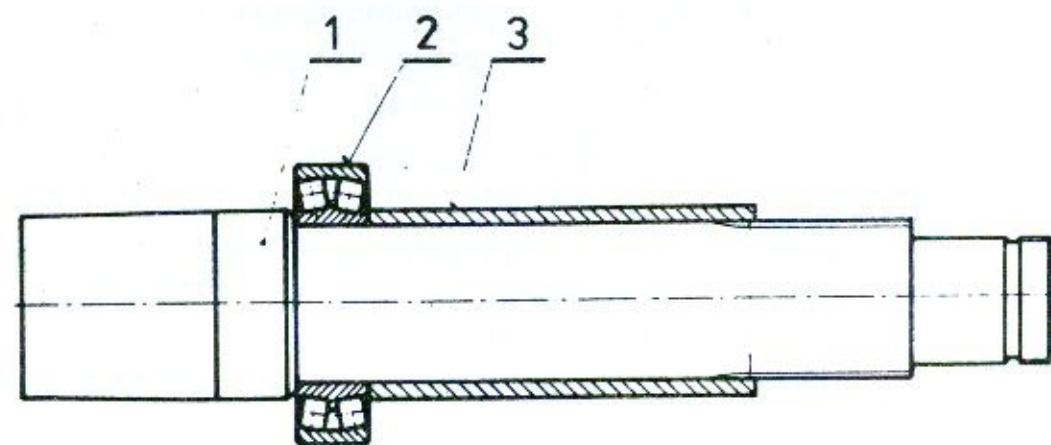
1 - валик, 2 - подшипник, 3 - распорная трубка
